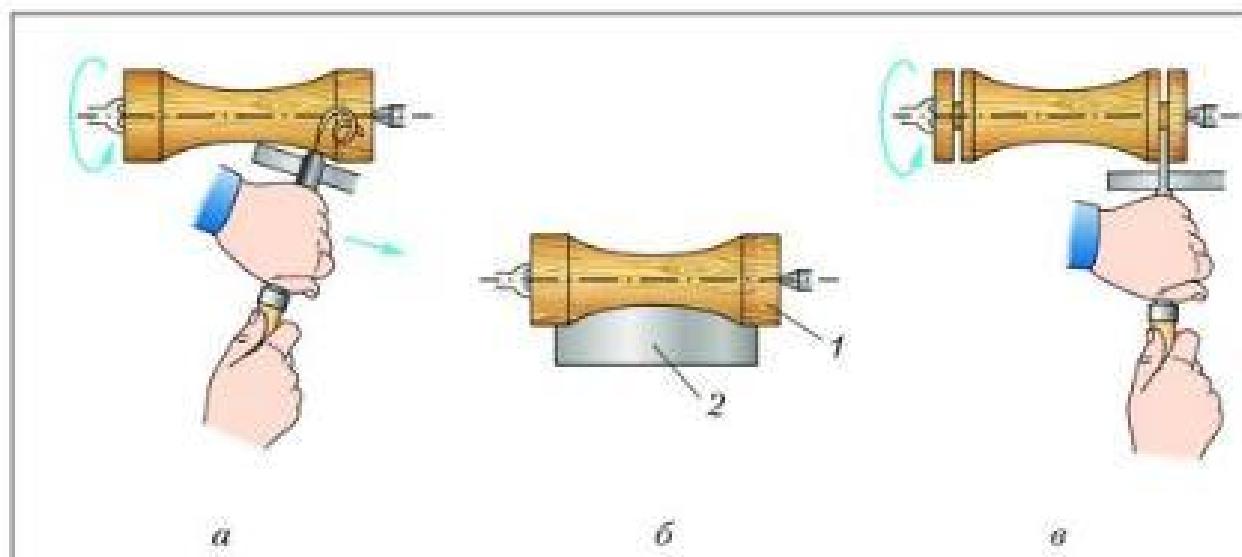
Обработка вогнутой поверхности: *а* — черновое точение; *б* — проверка формы поверхности шаблоном; 1 — заготовка; 2 — шаблон; *в* — проточка канавок
